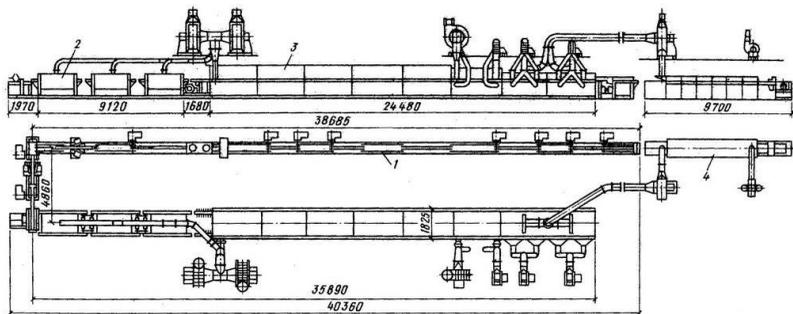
Конвейер для производства литых плиток: 1 – литейный конвейер; 2 – сушилка; 3 – щелевая роликовая цепь; 4 – конвейер сушки и зачистки
